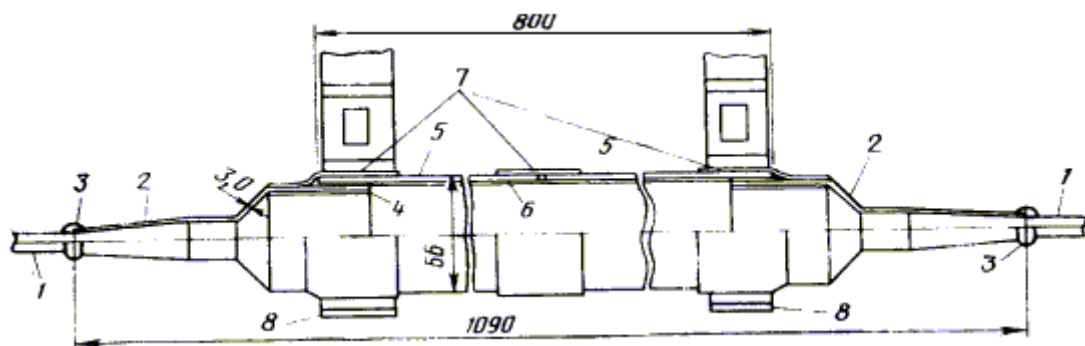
Готовая муфта: 1 – оптический кабель; 2 – полиэтиленовые конусы; 3 – приварка конусов к оболочке кабелей методом наплавления полиэтиленовой ленты под стеклолентой; 4 – опорные стальные втулки; 5 – полиэтиленовые цилиндры; 6 – металлический желобок; 7 – пояски из отрезков термоусаживаемых трубок 80/40; 8 – кабельные консоли
